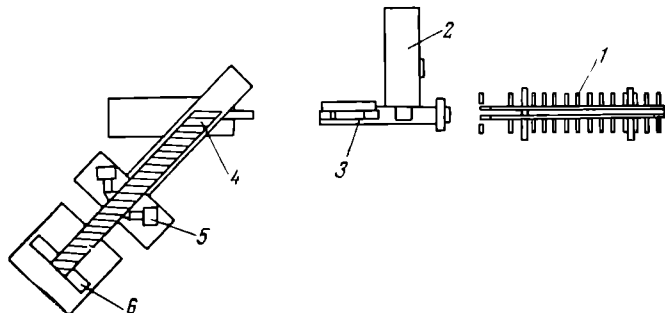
Схема поточной линии для выпуска брекерных заготовок из металлического корда: 1 — шпулярик; 2, 5 — червячные машины; 3 — охлаждающие барабаты; 4 — раскройно-стыковочный автомат; 6 — закаточное устройство.
